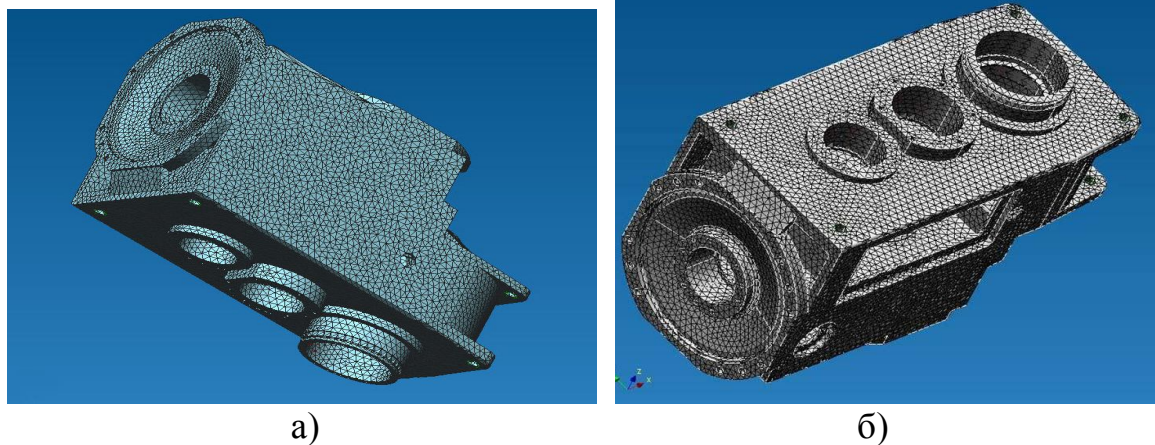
Конечно-элементная модель: а) корпус цилиндрического редуктора, б) корпус коническо-цилиндрического редуктора
